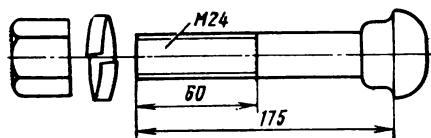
Стыковой болт с гайкой и пружинной шайбой
